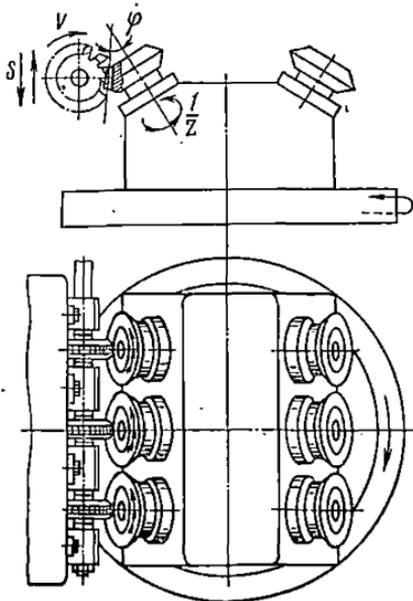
Черновая обработка конических зубчатых колес дисковыми фрезами.
